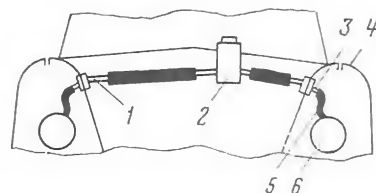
Схема автоматической прокачки и долива амортизаторов: 1 — трубка; 2 — наполнительный бачок; 3 — штуцер; 4 — крыло; 5 — шланг; 6 — амортизатор.
